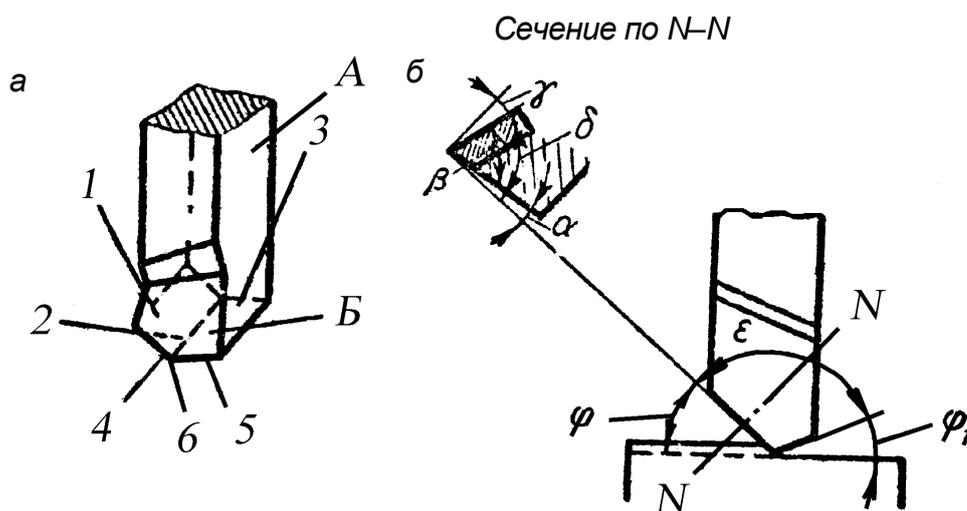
Строгальный резец: а – основные части и элементы; б – углы резца; 1 – передняя поверхность головки резца; 2 – главная поверхность; 3 – вспомогательная поверхность; 4 – главная режущая кромка; 5 – вспомогательная кромка; 6 – вершина
